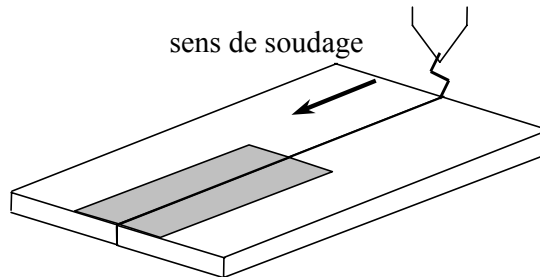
Configuration de soudage TIG-ATIG
